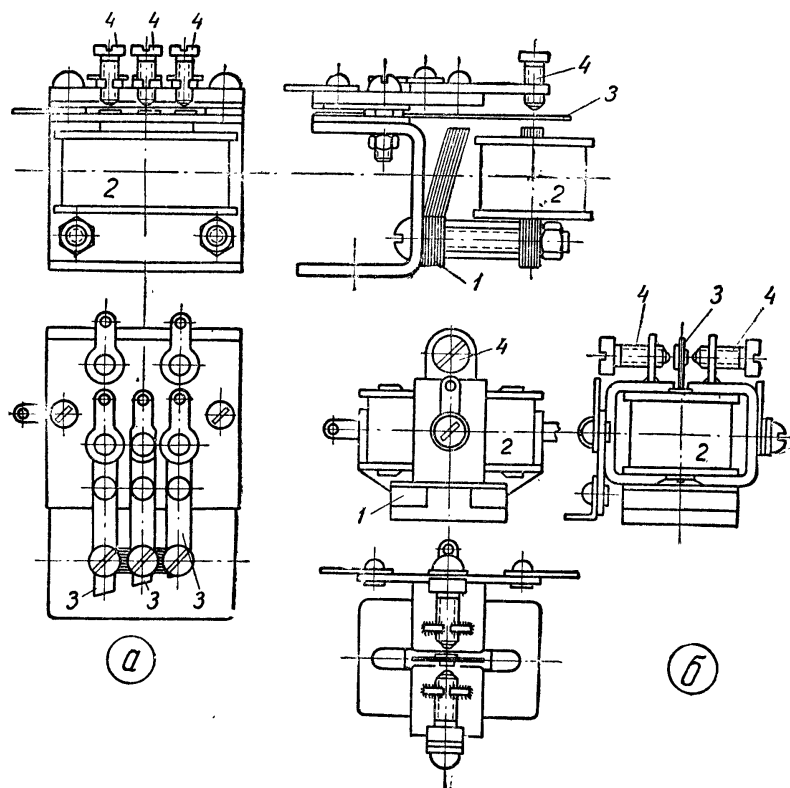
а — резонансное реле; 1 — магнитопровод; 2 — обмотка; 3 — якорь реле; 4 — регулировочные винты контактов; б — поляризованное реле; 1 — постоянный магнит; 2 — обмотка; 3 — якорь реле; 4 — регулировочные винты контактов.
